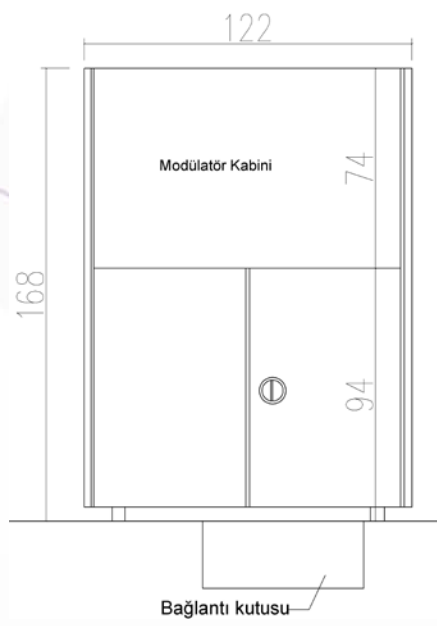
Modülatör Kabini Plan Görünümü (Ölçeksiz)
